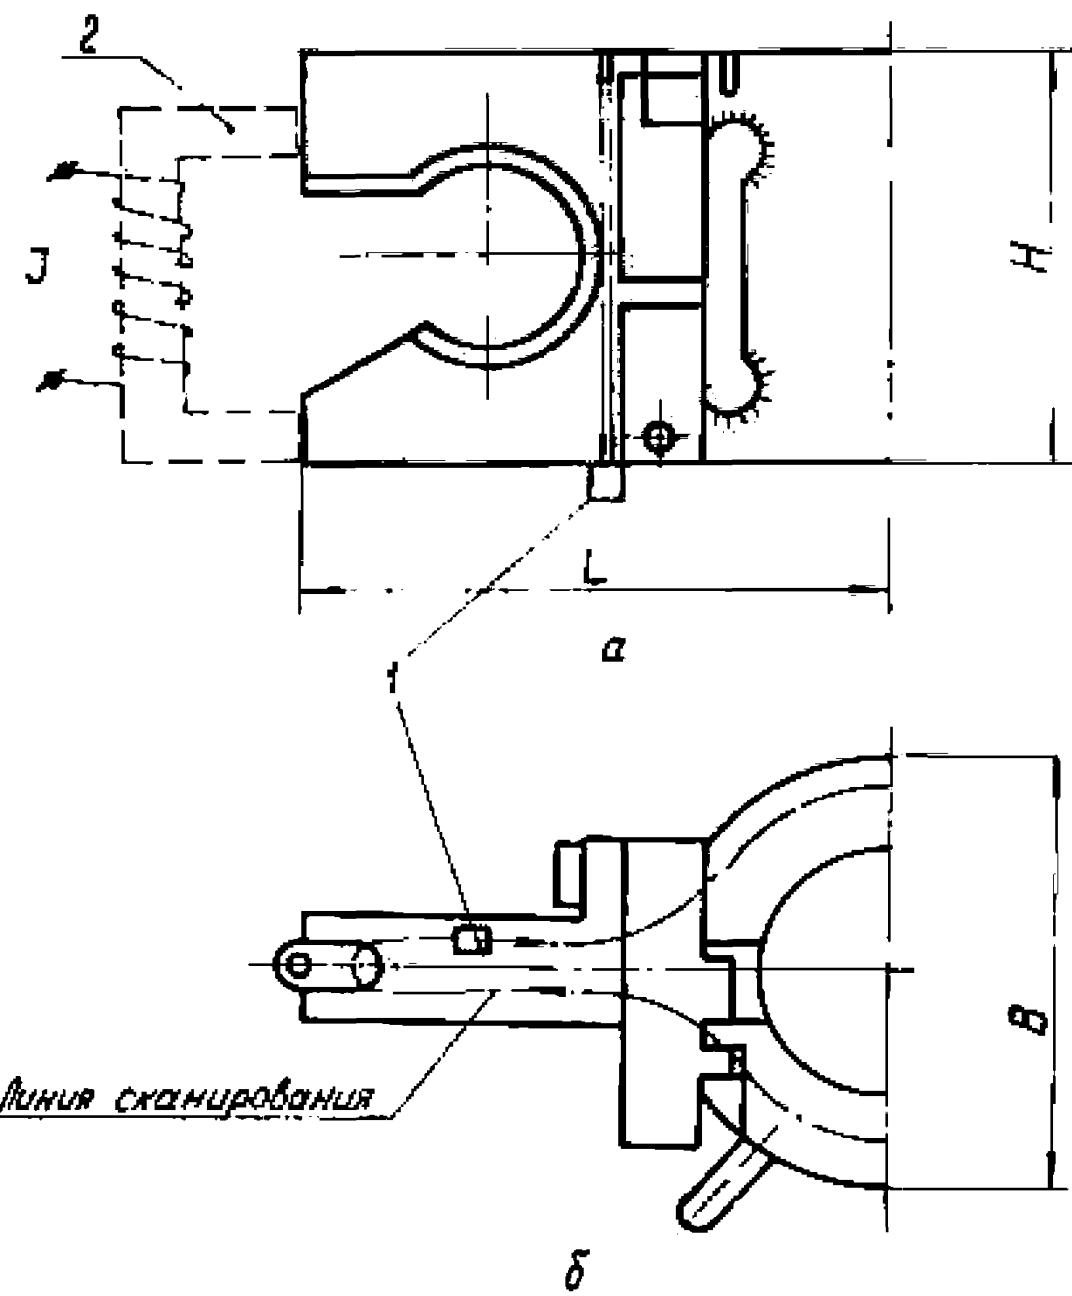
Схема контроля элеватора магнитопорошковый (а)
